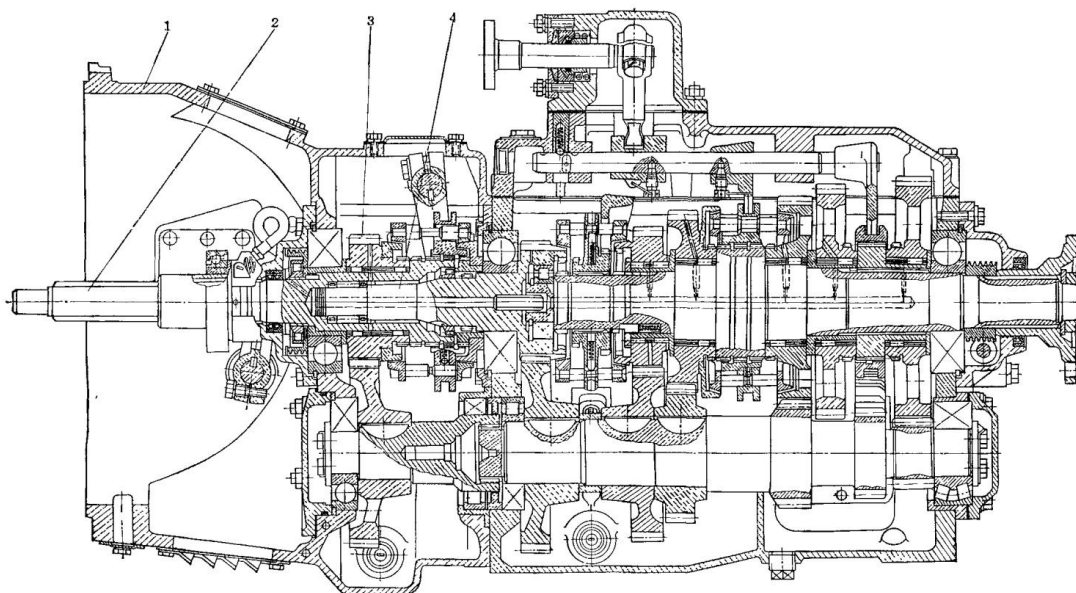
10-ступенчатая коробка передач автомобиля КамАЗ-5320
